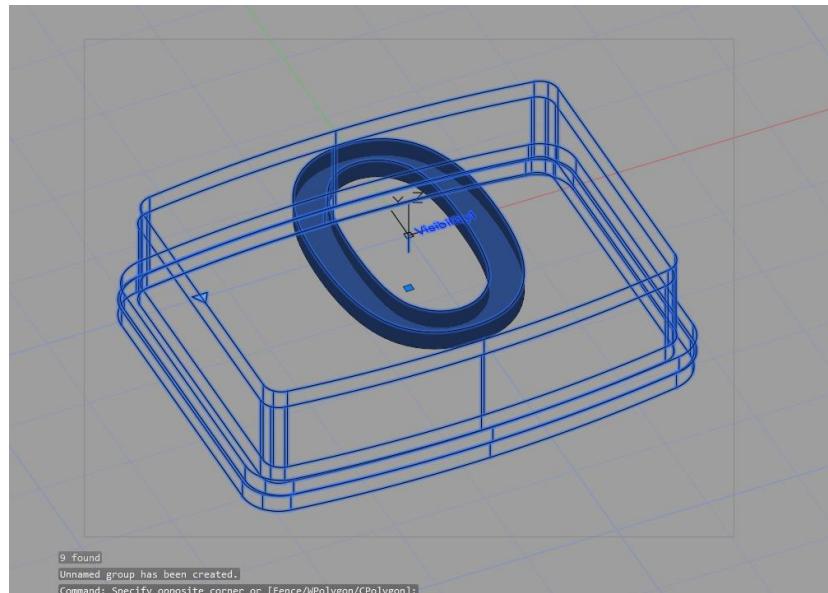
Gruparea elementelor pentru a facilita următoarea etapă
